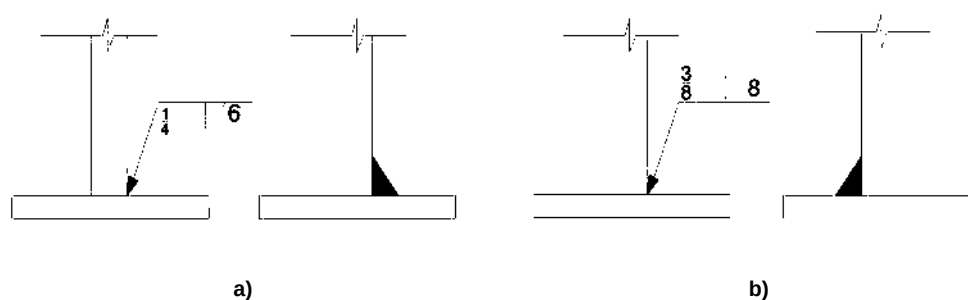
9 Juntas de soldadura (Modificado de Jack, C. & Stephen, F. 2012).
